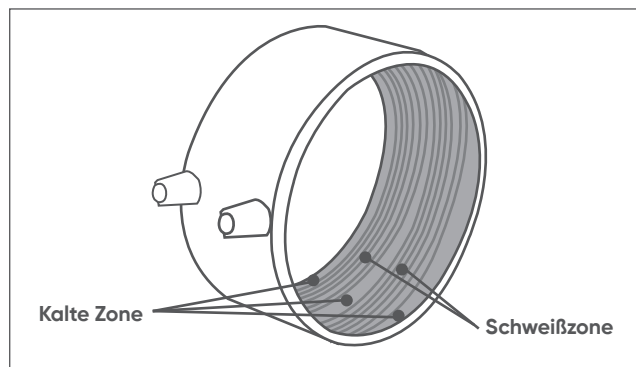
Elektroschweißmuffe mit kalter Zone und Schweißzone
